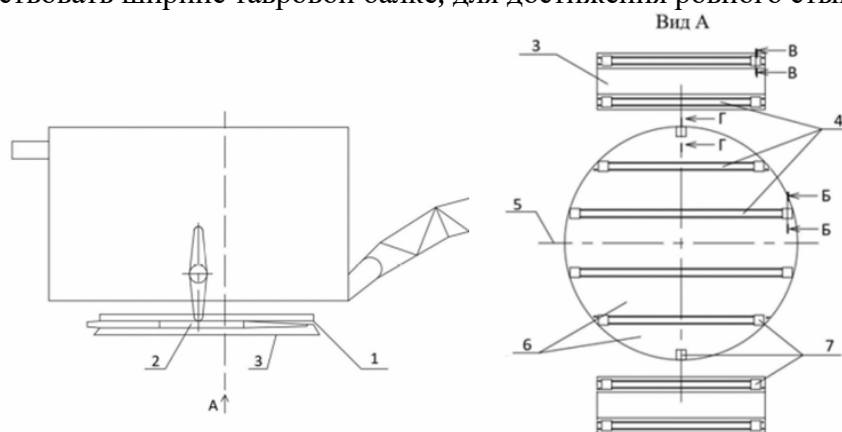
Фронтальный вид экскаватора и вид А с расположением прорезей для балок на лыжах и опорной базе: 1 – опорная база экскаватора; 2 – поворотная платформа; 3 – лыжи; 4 – прорезы; 5 – продольная ось экскаватора; 6 – сегменты днища; 7 – П-образный профиль.
